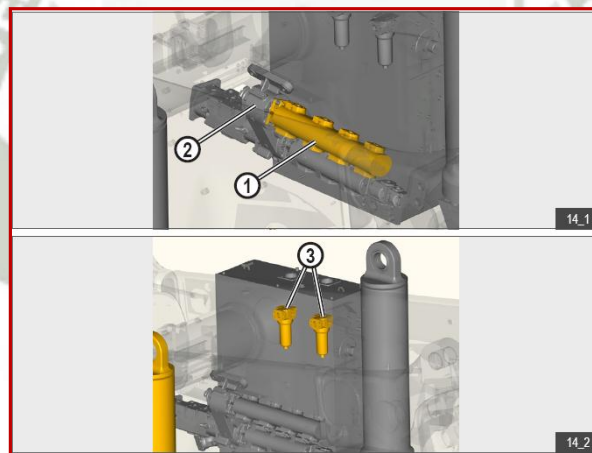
Bomba de Engranajes del Sistema de Levante
